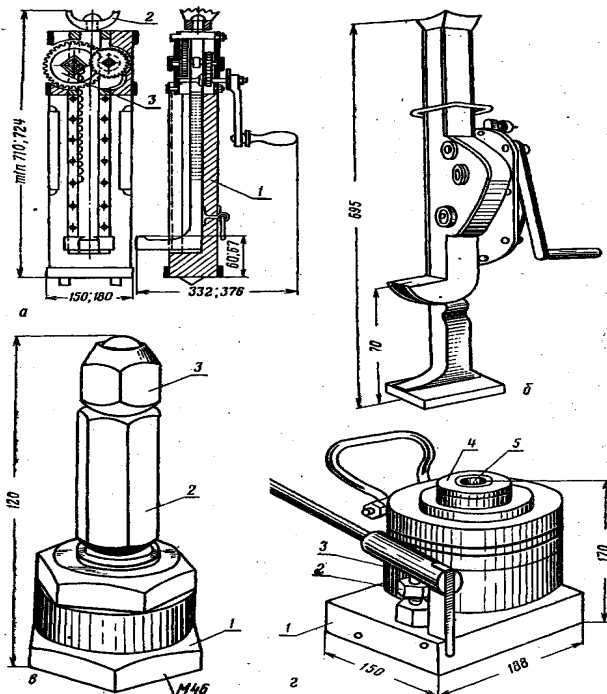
Вантажопідійомні домкрати: а – рейковий з шестерним приводом; 1 – зубчаста рейка з лапою; 2 – поворотна головка; 3 – зірочка; б – рейковий з храповим приводом; в – гвинтовий; 1 – опорна гайка; 2 – підйомний гвинт; 3 – опорна головка; г – полегшений гідравлічний; 1 – плита; 2 – одноплунжерний ручний насос; 3 – корпус; 4 – циліндр; 5 – поршень.
